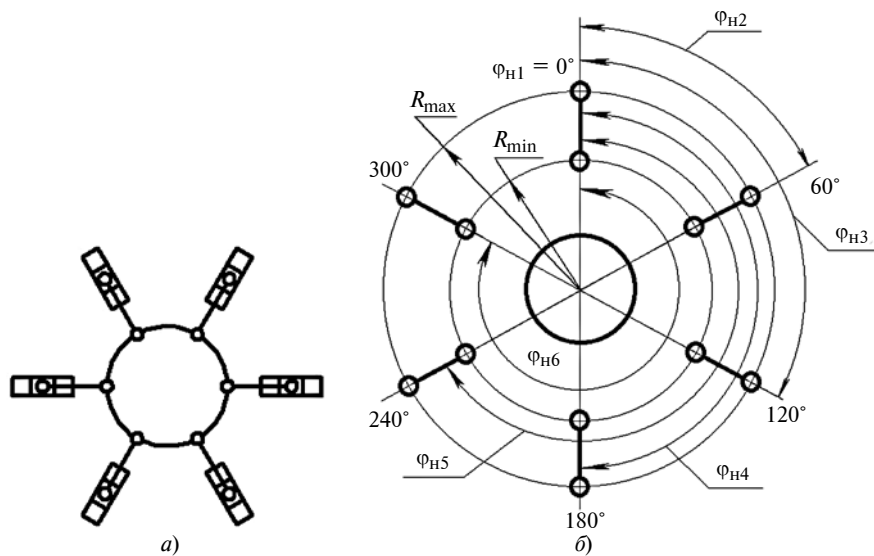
Схема (а) и компоновочные параметры механизма с равномерным размещением шести направляющих (б)
